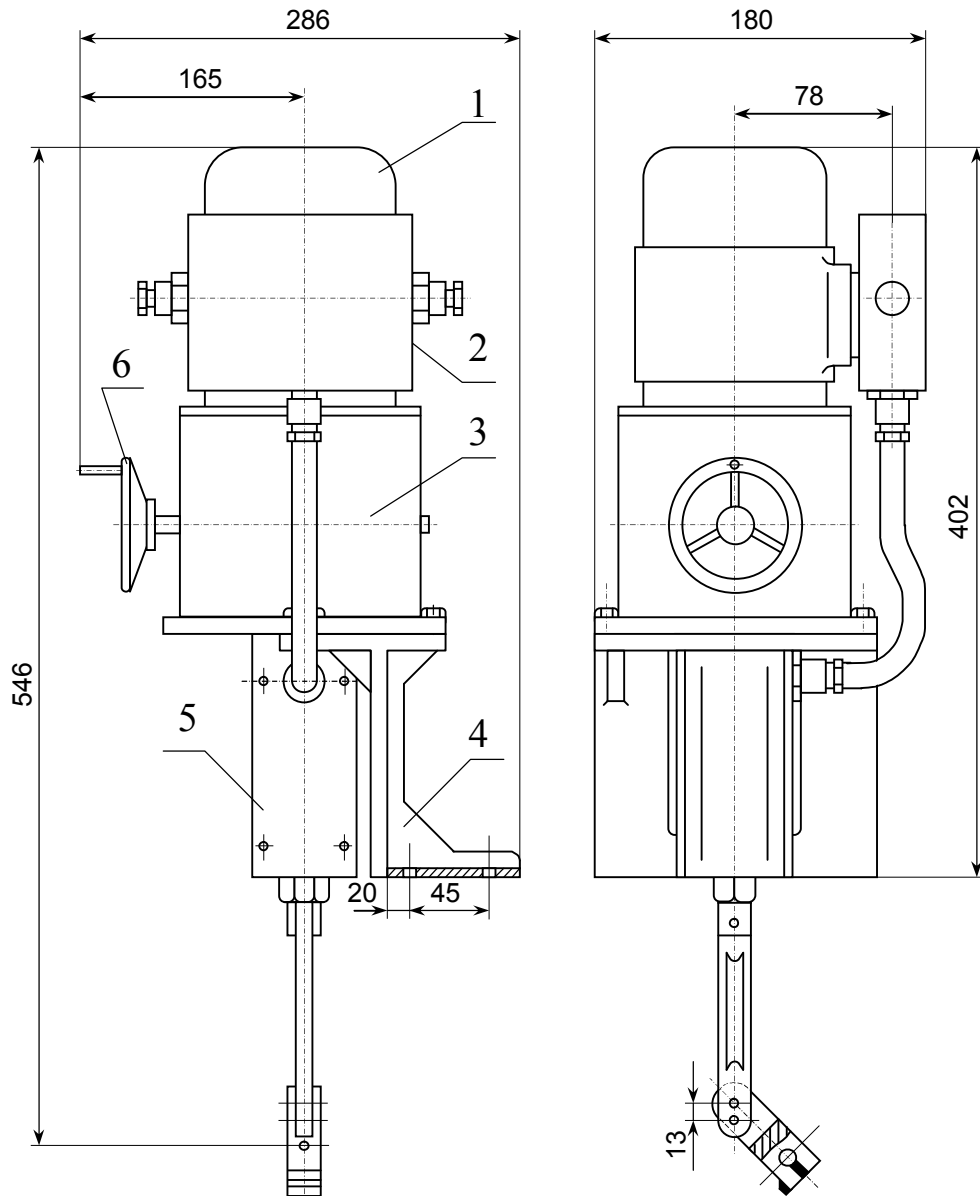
Габаритні розміри механізму типу ЕСПА: 1- електродвигун; 2 – розподільча коробка; 3 – редуктор; 4 – стійка; 5 – керуюча коробка; 6 – ручний дублер.
